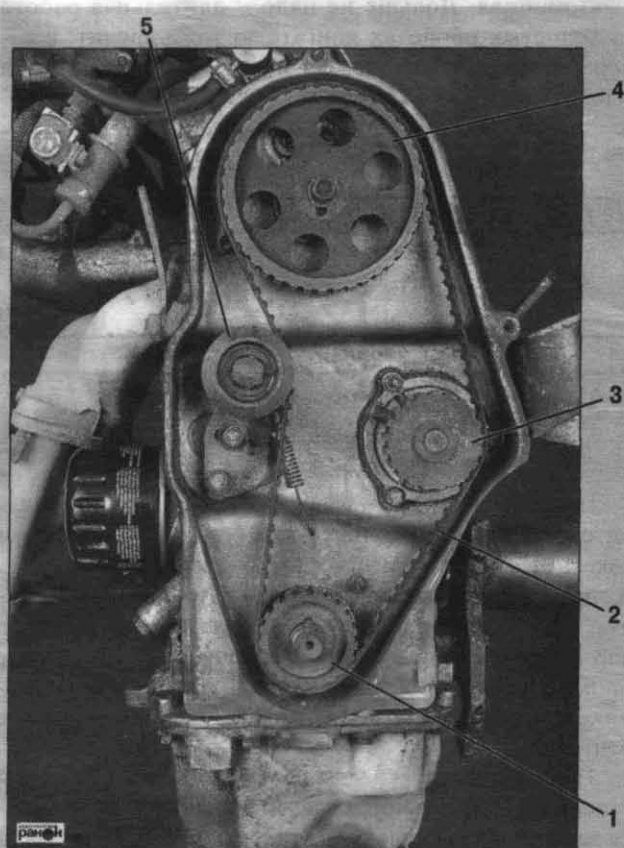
Схема привода ГРМ: 1 – шкив коленвала; 2 – ремень ГРМ; 3 – насос охлаждающей жидкости («помпа»); 4 – шкив распредвала; 5 – натяжной ролик
